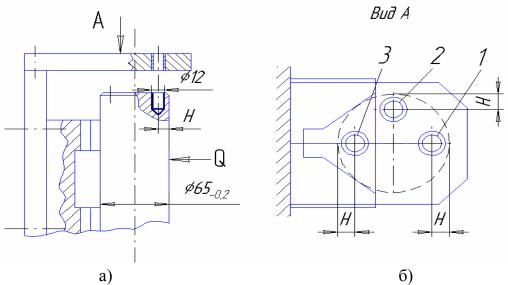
Схемы установки кондукторной втулки: a — для сверления наиболее удаленного от призм отверстия 1; б — возможные варианты установки кондукторной втулки для сверления отверстий 1, 2, 3
